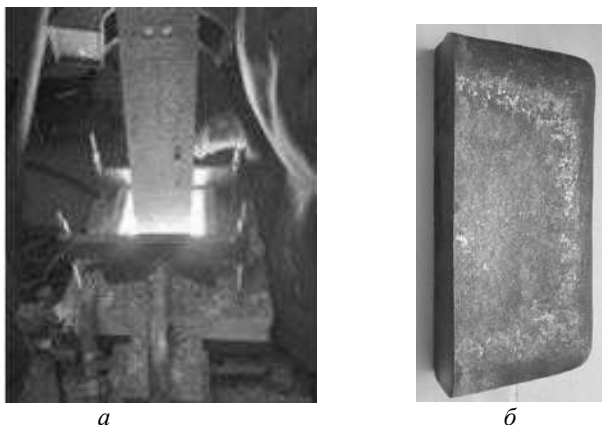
Процес наплавлення металу з використанням СПК квадратного поперечного перерізу із застосуванням полого наплавного електрода квадратного поперечного перерізу (а), наплавлений біметалевий армуючий елемент, розрізаний навпіл (б)
